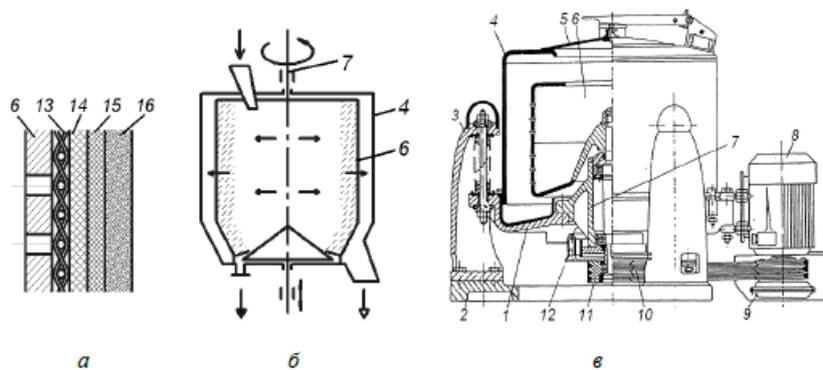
Схема фильтрующей маятниковой центрифуги (а, б) и ее сборочный чертеж (в): 1, 2 – станина; 3 – подвеска; 4 – кожух; 5 – крышка; 6 – ротор; 7 – подшипниковый узел; 8 – электродвигатель; 9, 10, 11 – клиноременная передача; 12 – основание; 13 – сетка; 14 – фильтрующая ткань; 15 – осадок; 16 – суспензия (рис. Н.А. Войнова)
